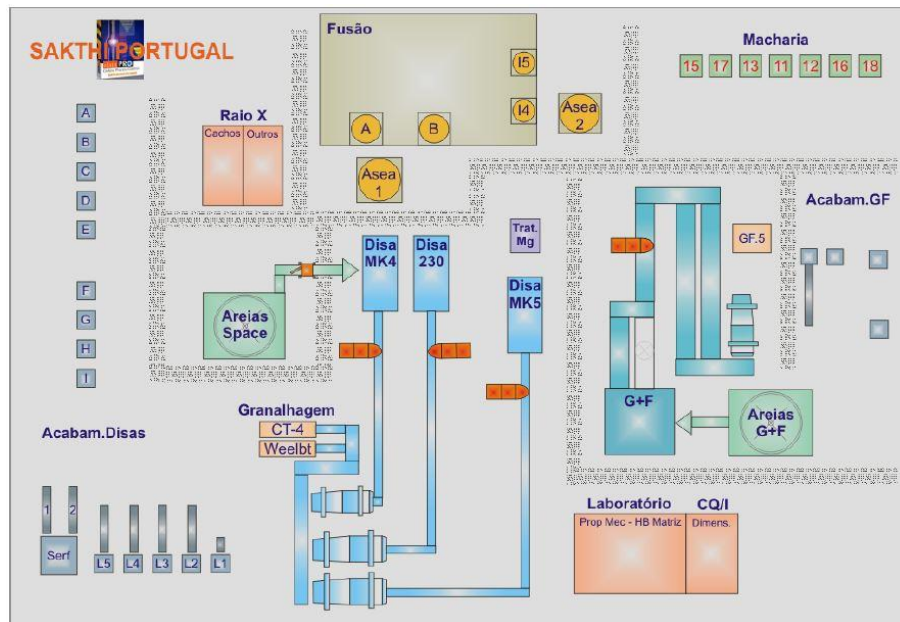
Planta da Área Fabril (retirado de (Portugal, 2013))
